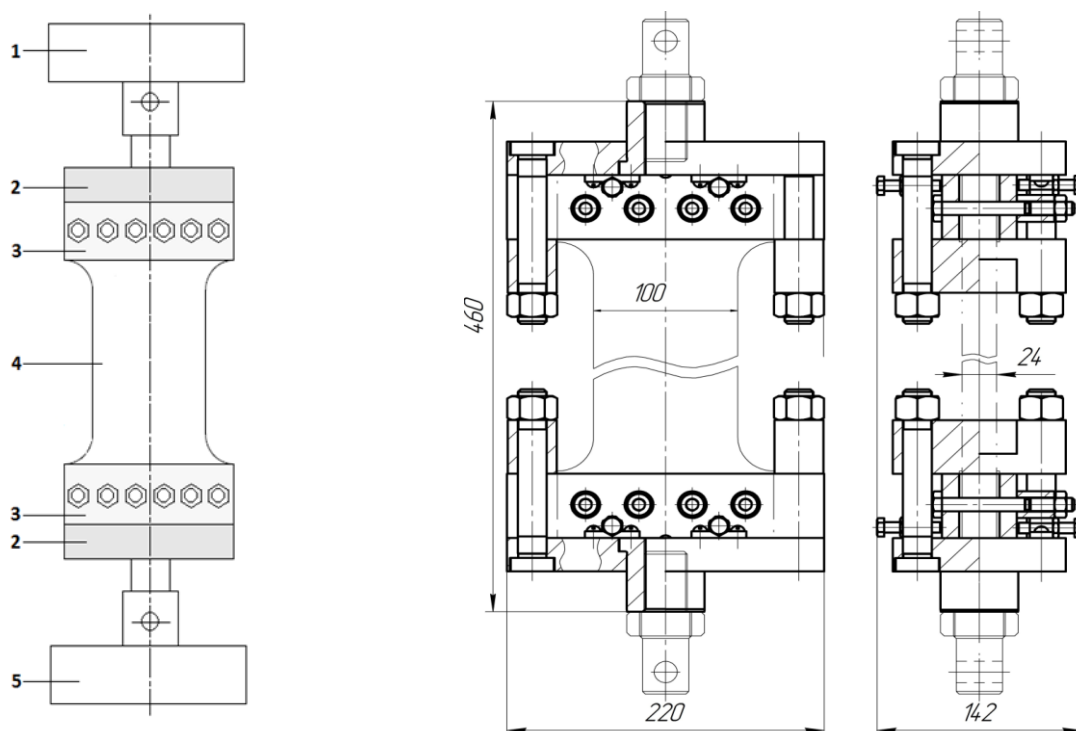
Схема закрепления и эскиз оснастки для проведения испытаний образцов-панелей на растяжение (1 – подвижная траверса; 2 – захваты; 3 – стальные пластины-накладки; 4 – образец; 5 – неподвижная траверса)
